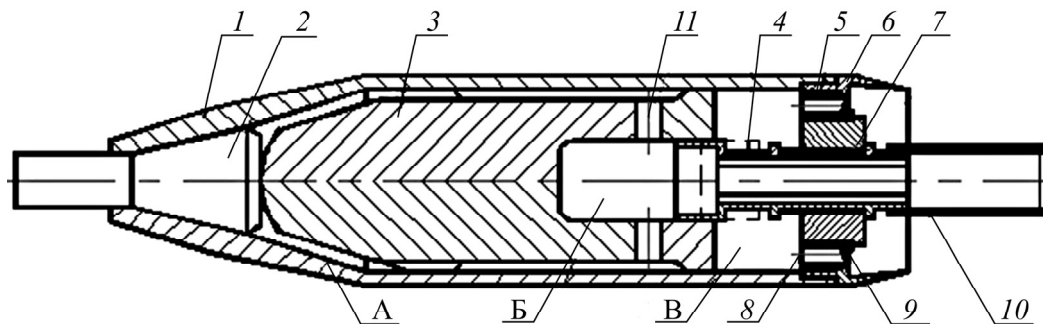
Принципиальная конструктивная схема пневмопробойника: 1 — корпус; 2 — наковальня; 3 — боек; 4 — патрубок; 5 — амортизатор; 6 — хвостовик; 7 — втулка; 8 — выхлопные каналы; 9 — клапаны на втулке; 10 — шланг; 11 — отверстия для сообщения камер А и Б; А — камера холостого хода; Б — камера рабочего хода; В — выхлопная камера
